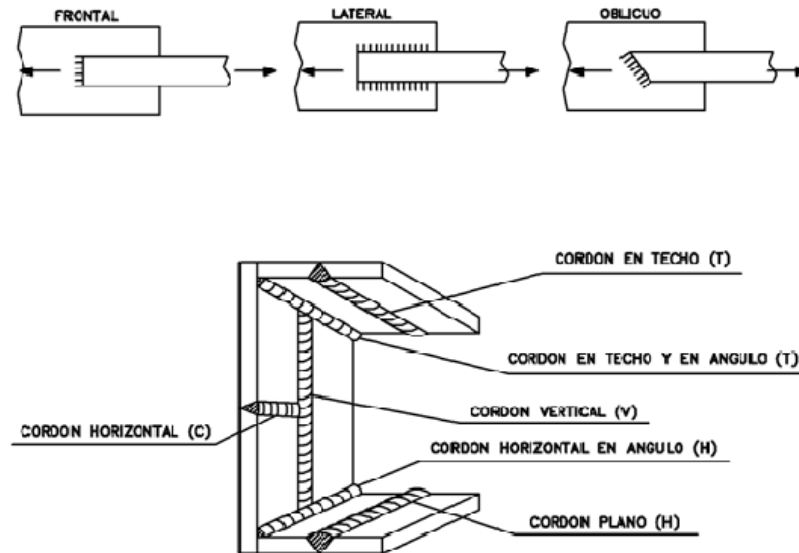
Tipos de cordones de soldadura [43]
